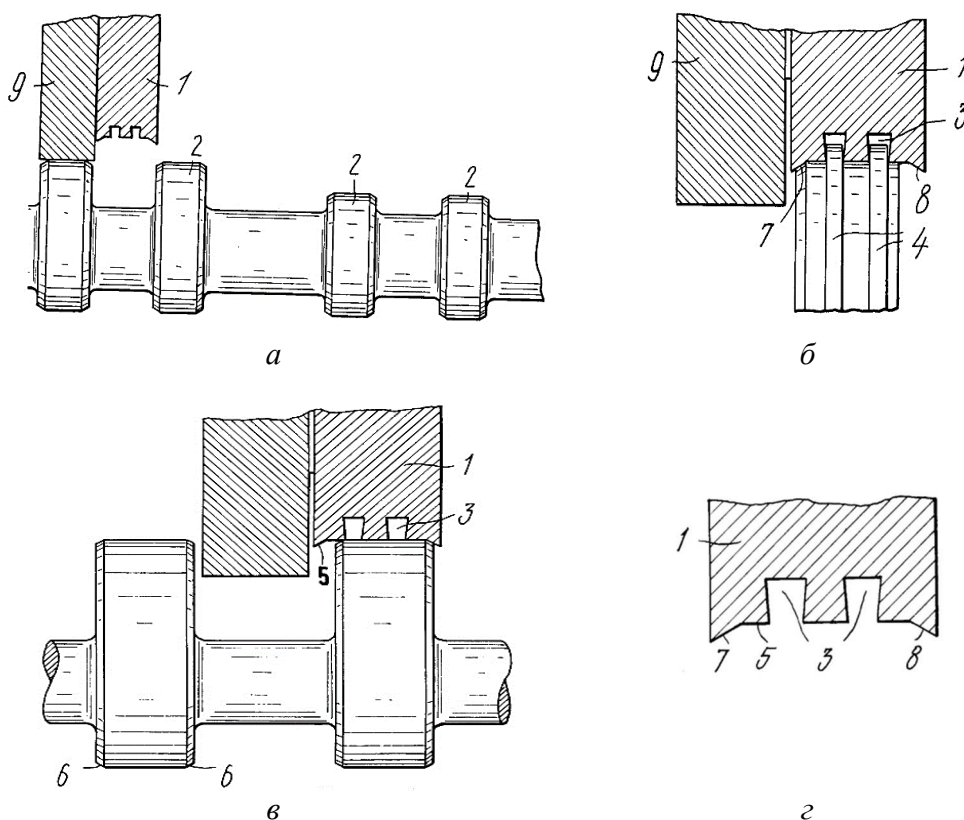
Схема обробки кулачків розподільного вала двома шліфувальними кругами:
